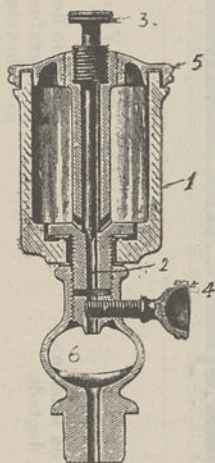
COPO COM REGULADOR DE GOTA VISIVEL
